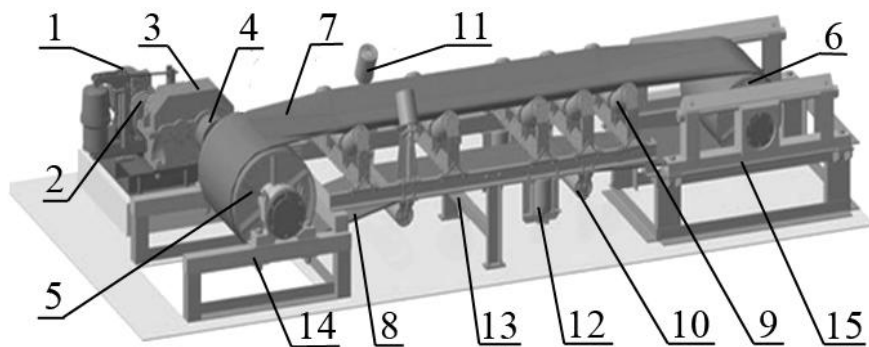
Конструкція та основні вузли стрічкового конвеєра
